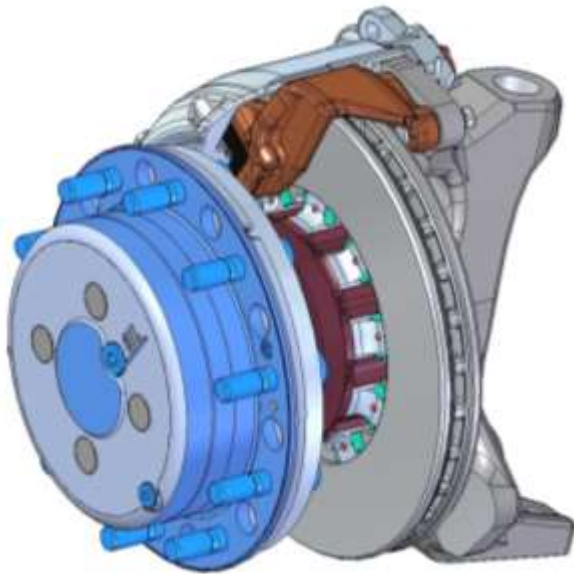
Radseitenausführung mit einem Radplanetengetriebe mit $i_{PI} = 4,36$ und einer Druckluftscheibenbremse
